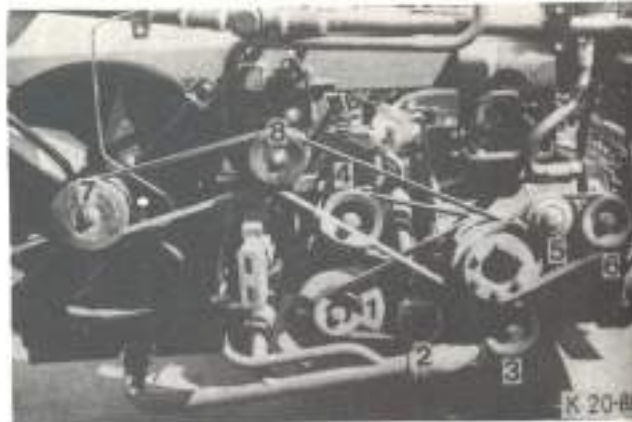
Клиноременная передача для типов 250/25 (K20-46)
